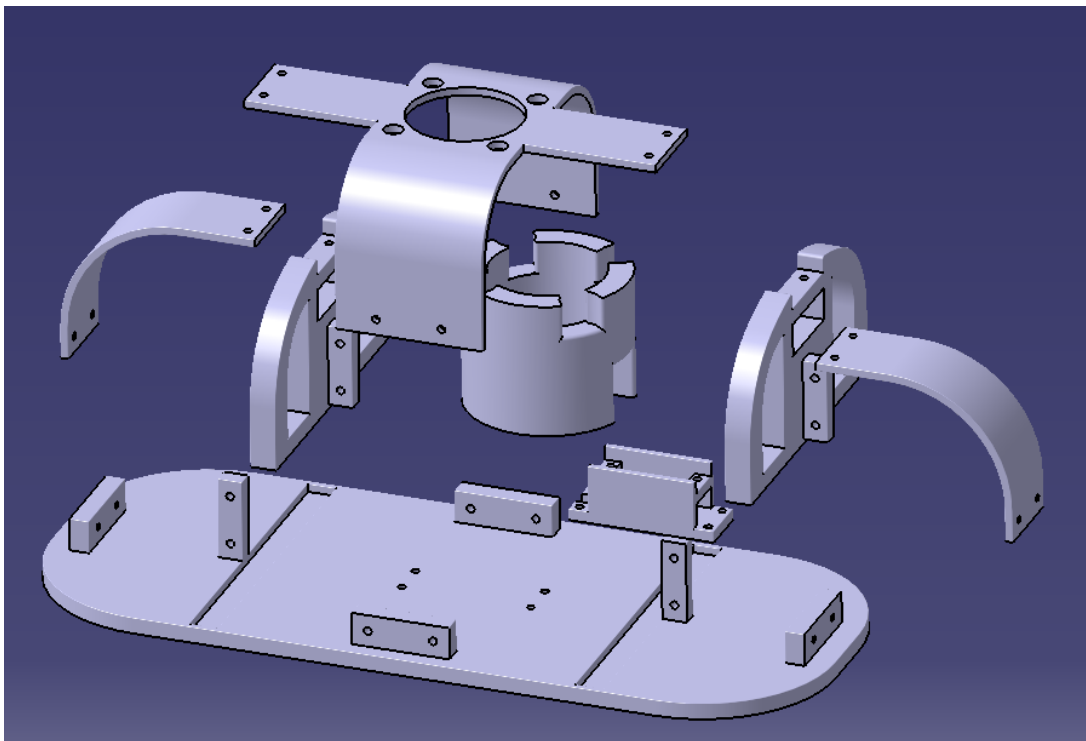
Despiece del conjunto de piezas del subensamblaje inferior.
